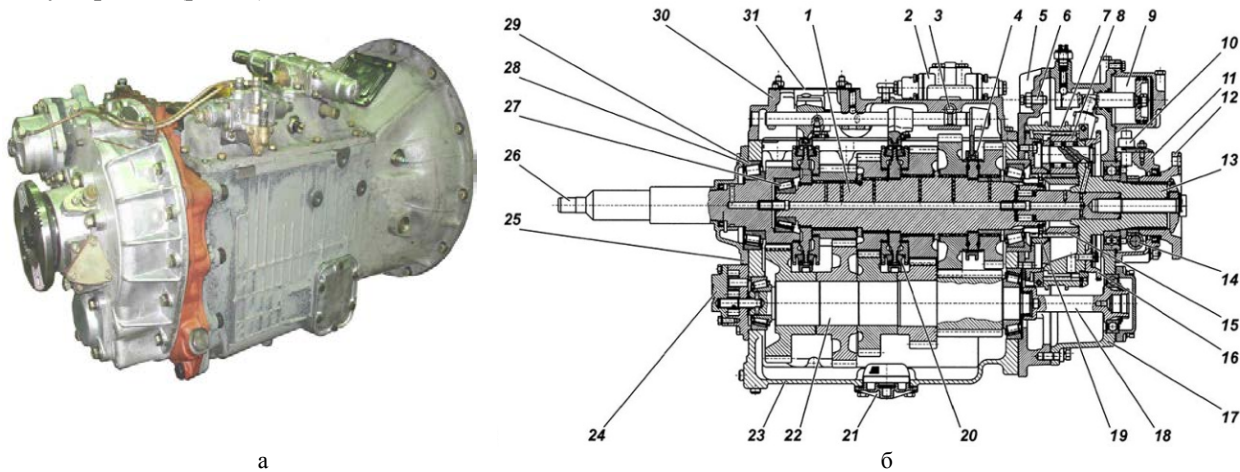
Коробка передач ЯМЗ-239 [10]: а — загальний вигляд; б — поперечний переріз;
